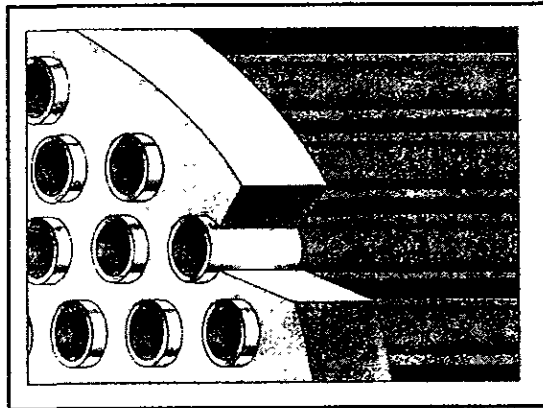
Unión tubo-espejo de un cambiador de calor.
